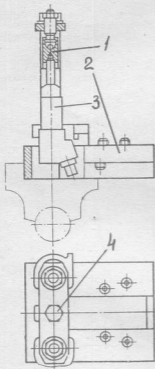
Приспособление И-801.20.000 для разборки форсунки:
